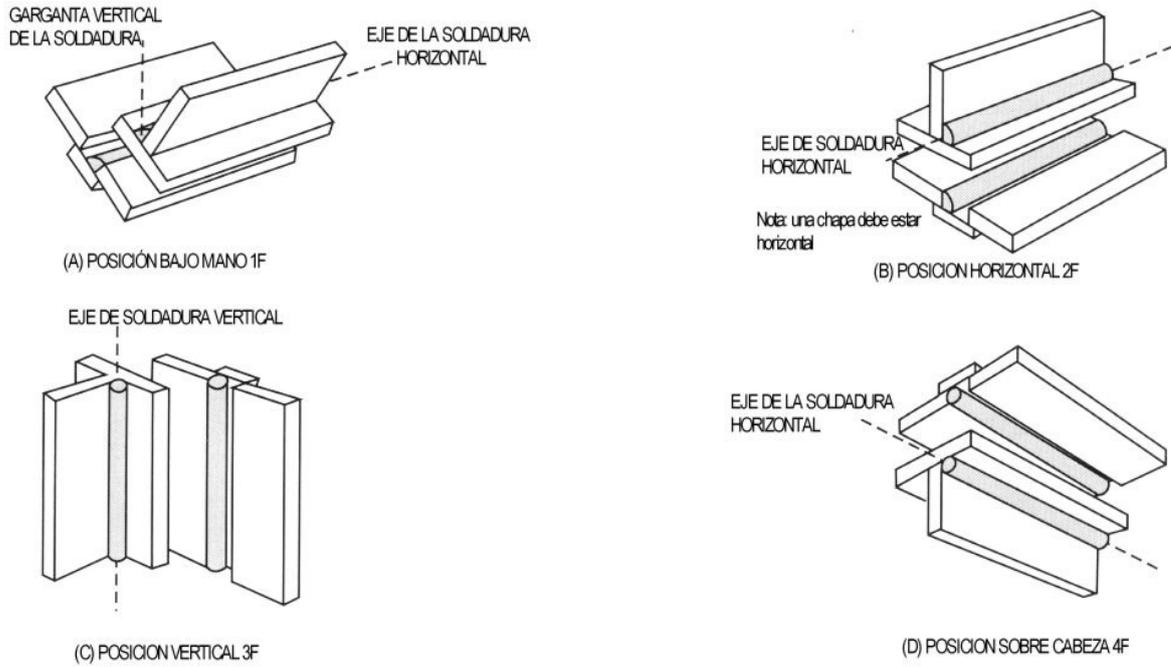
Posiciones de ensayo de chapa para soldaduras de filete
